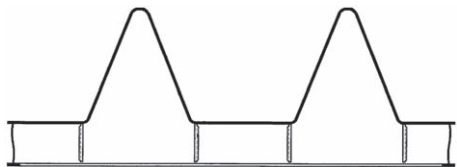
Вариант исполнения конструкции ледового пояса с гофрированными балками
